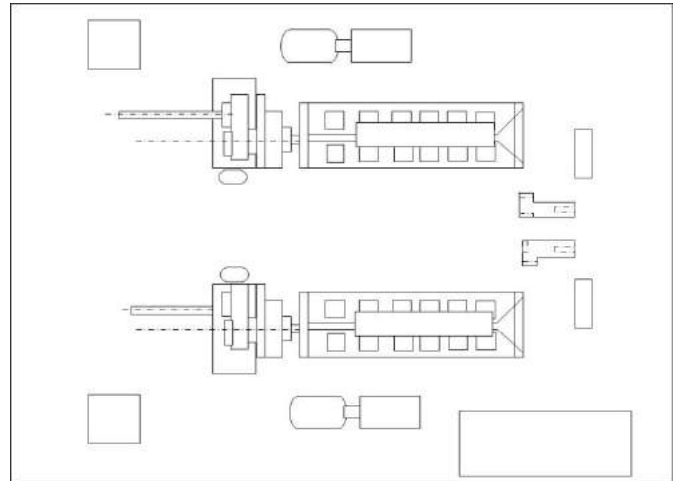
General Arrangement Plan KRI OWA – 354
